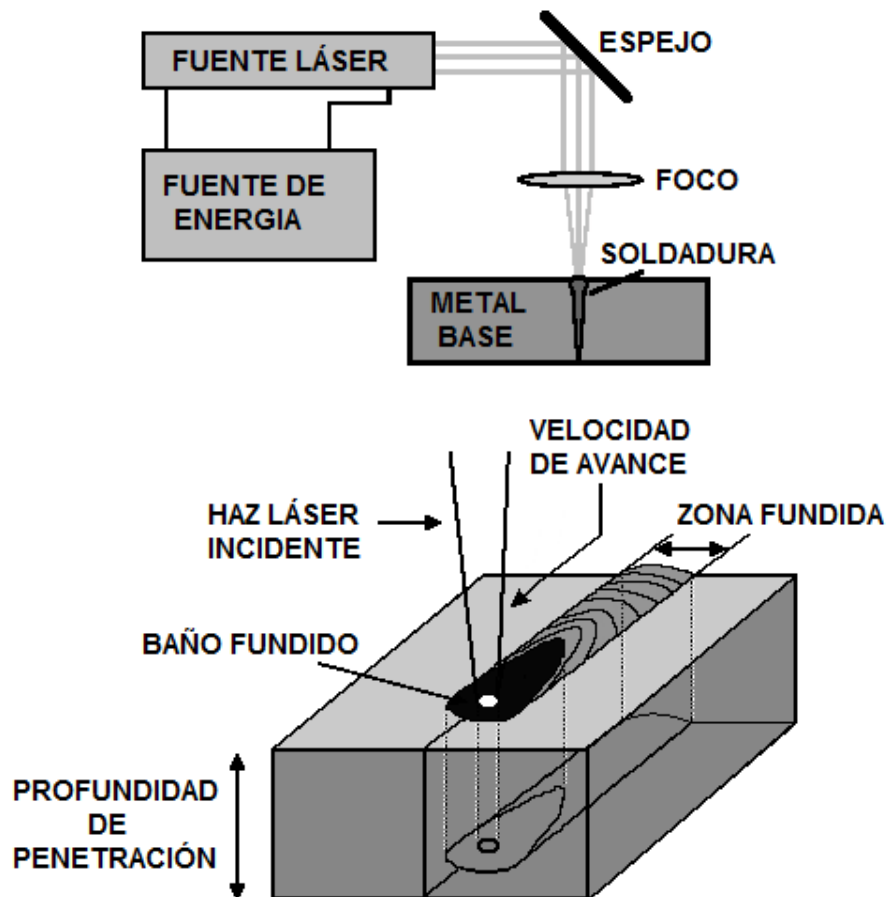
Esquema del proceso de soldadura por rayo láser (8, 18)
